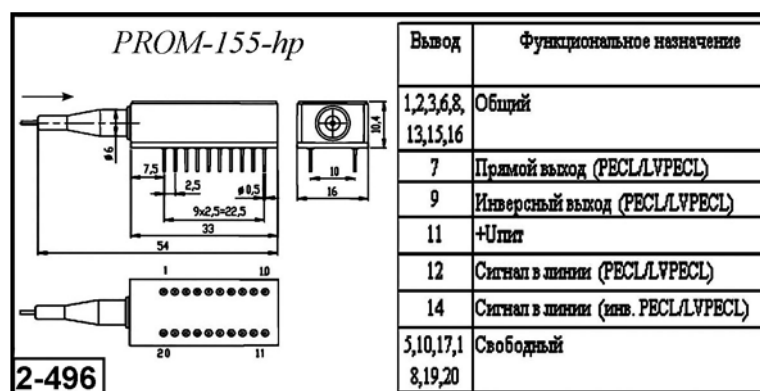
Внешний вид и габаритные размеры модуля PROM-155-hp
